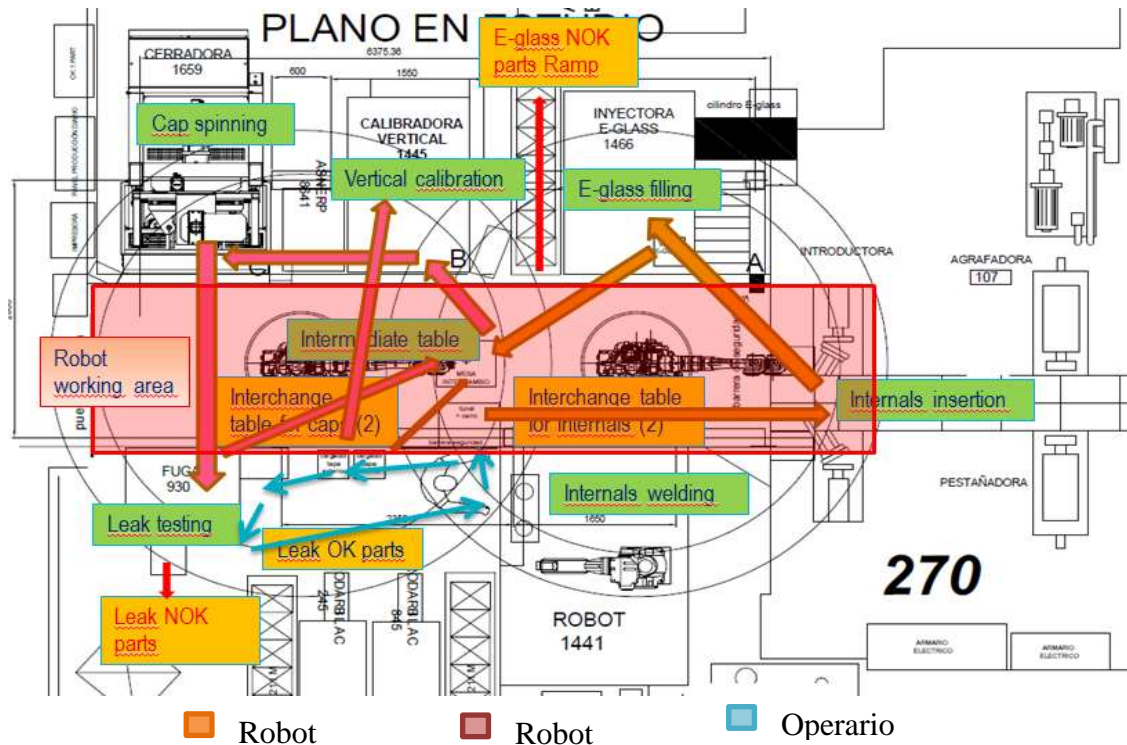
Secuencia de operaciones sobre la distribución en planta
